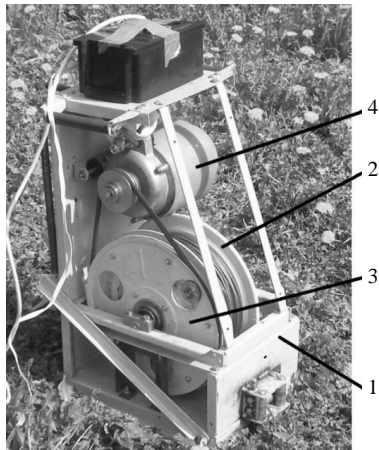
Общий вид сельскохозяйственной лебедки, разработанной на основе прецессионного редуцирующего механизма: 1 – корпус лебедки; 2 – барабан с прецессионным редуктором; 3 – шкив; 4 – электродвигатель
